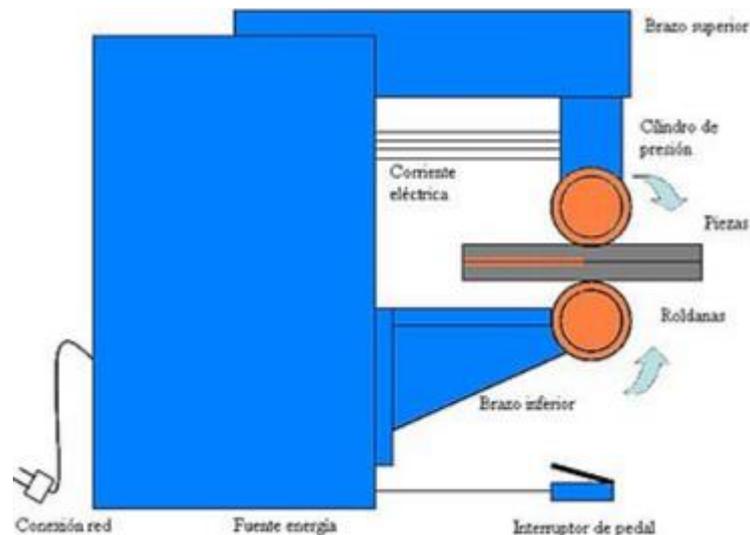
Máquina de soldadura por costuras. [3]
